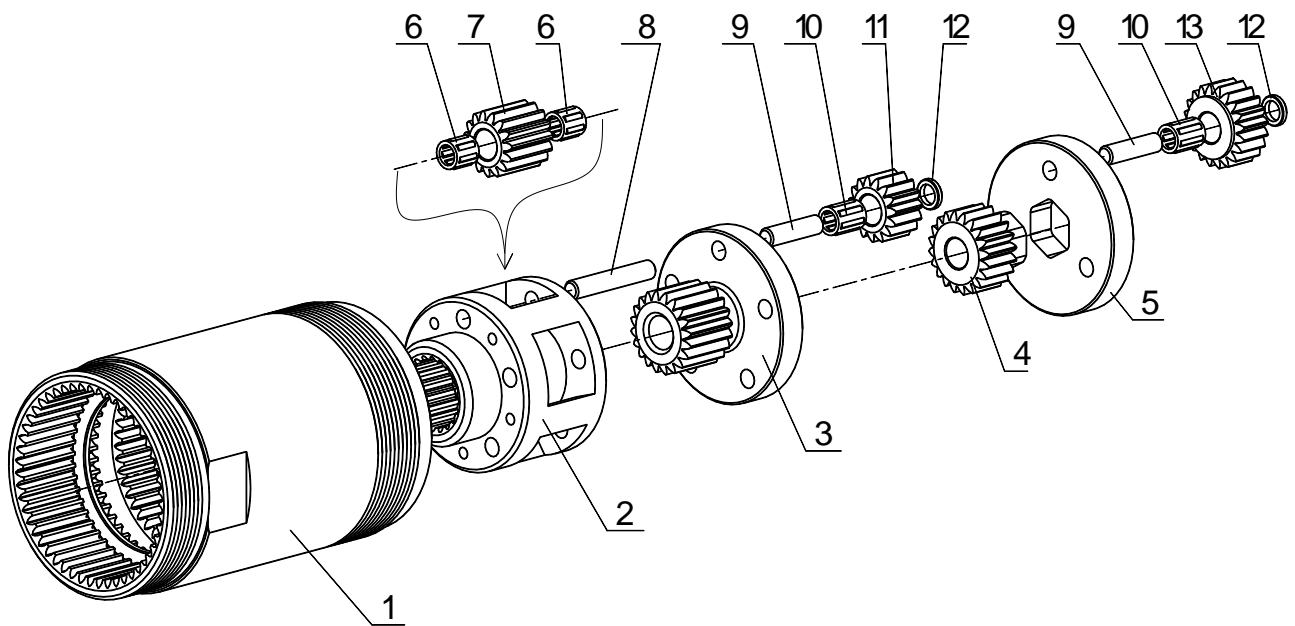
Редуктор планетарный трехступенчатый P233.00
